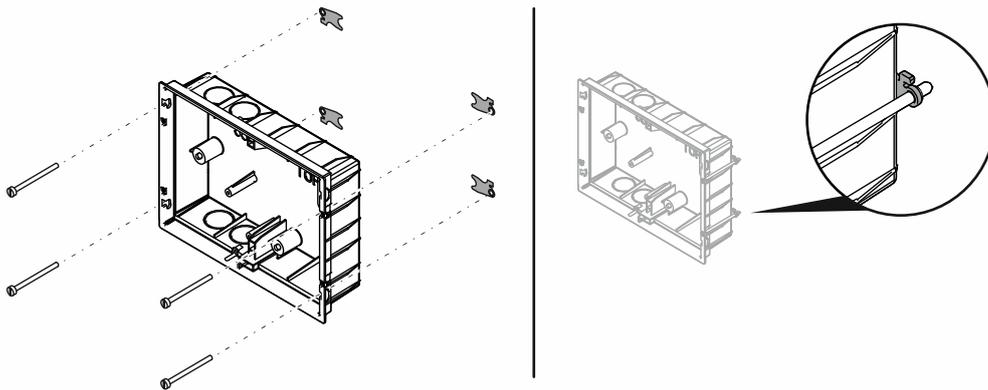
Montageset für Hohlwanddosen (83511-500)
